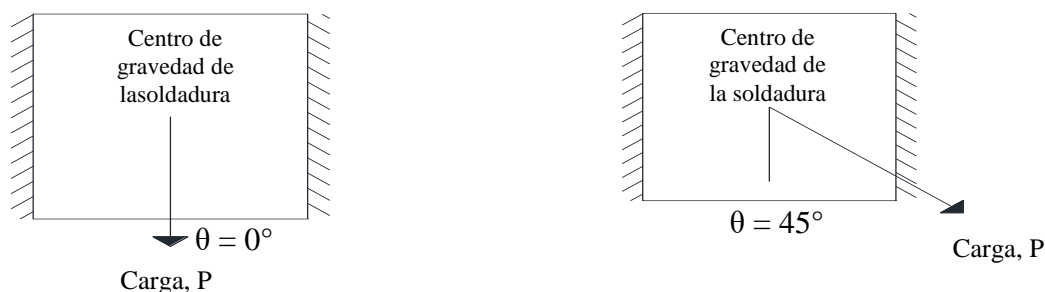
10 Centro de gravedad de la soldadura de filete
